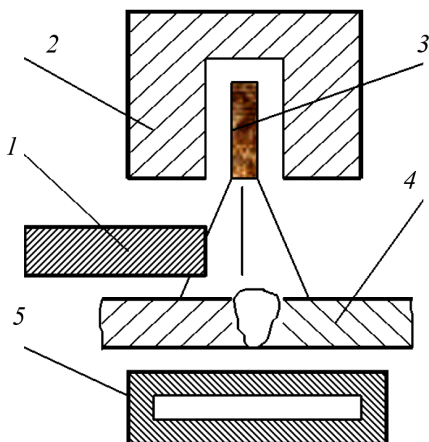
Схема просвечивания гамма-лучами: 1 – затвор; 2 – свинцовая капсула; 3 – капсула с радиоактивным веществом; 4 – сварное соединение; 5 – кассета с пленкой
